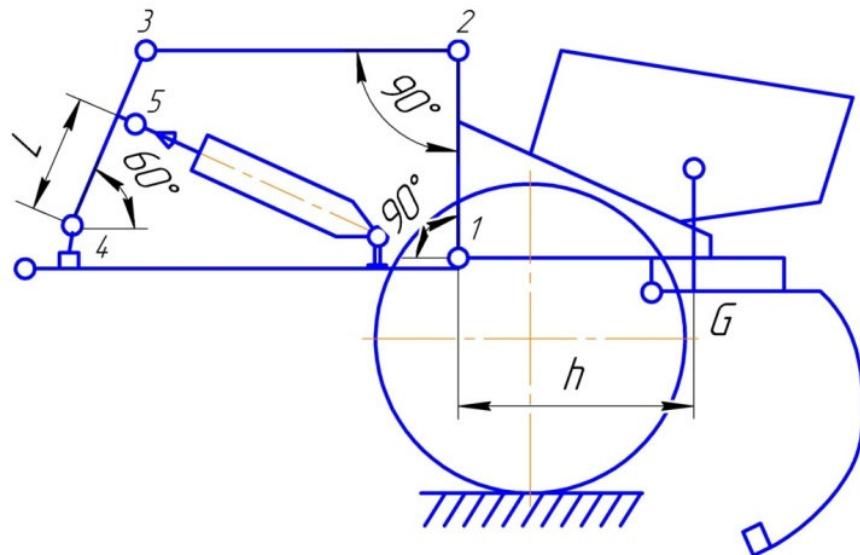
Схема гидрофицированного механизма подъёма штангового культиватора
